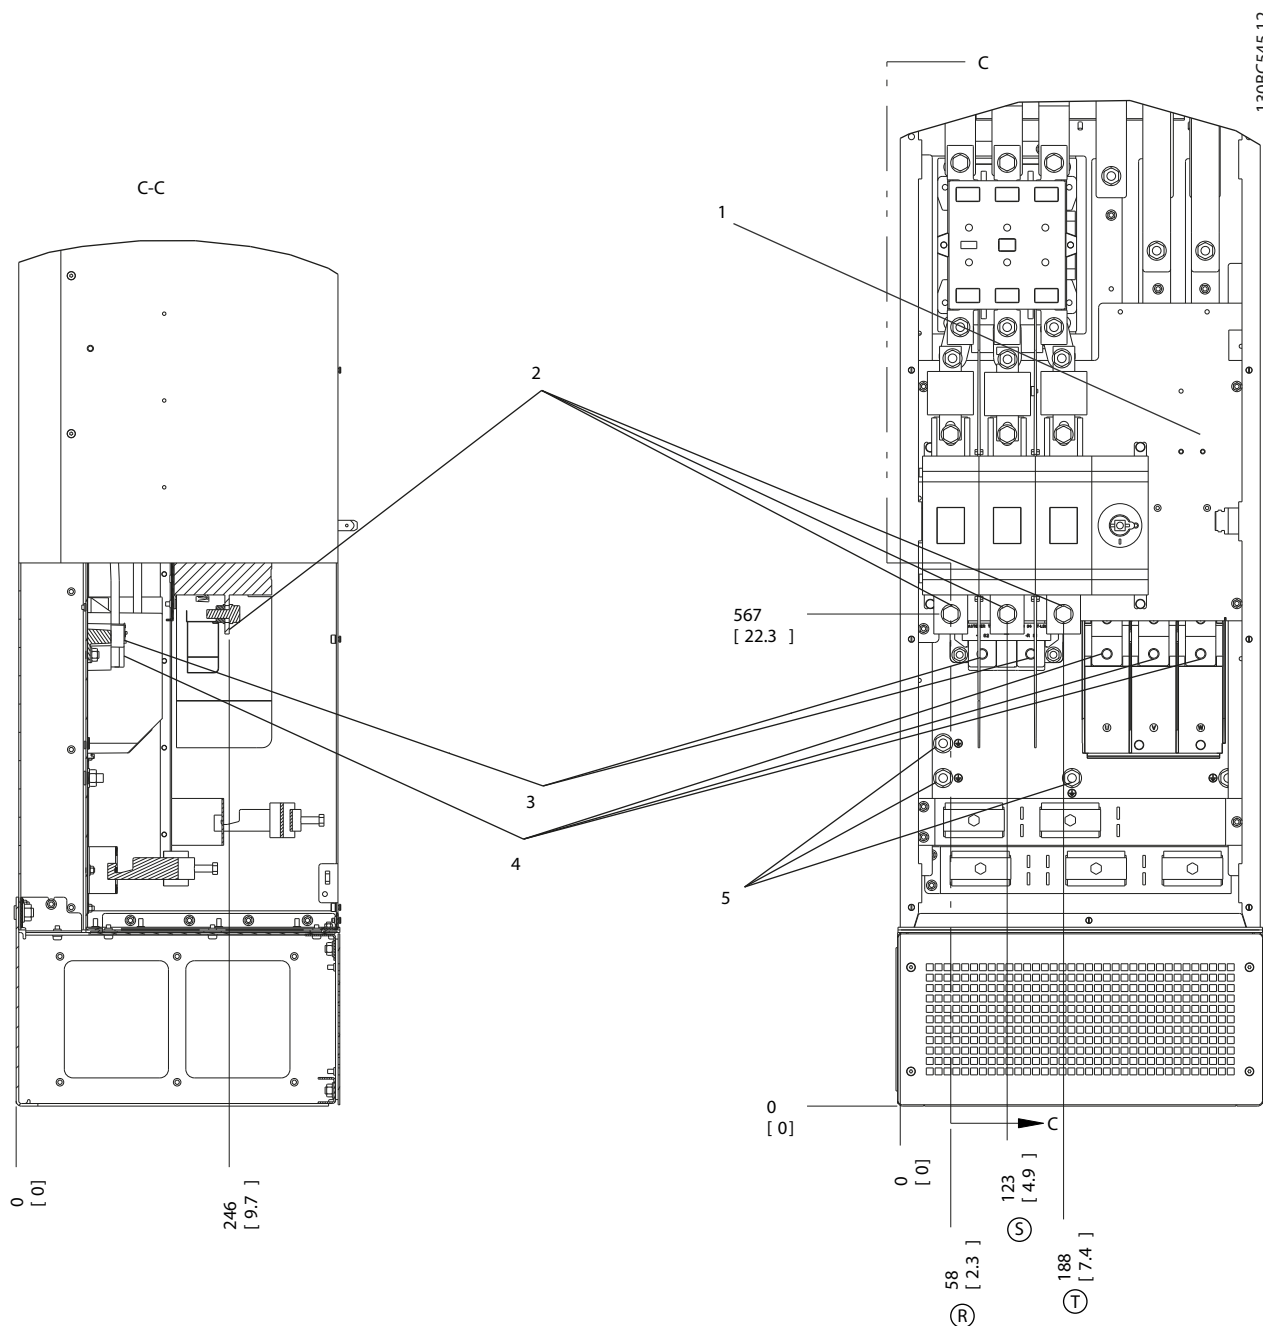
Расположение клемм, D8h с дополнительными устройствами контактора и разъединителя
